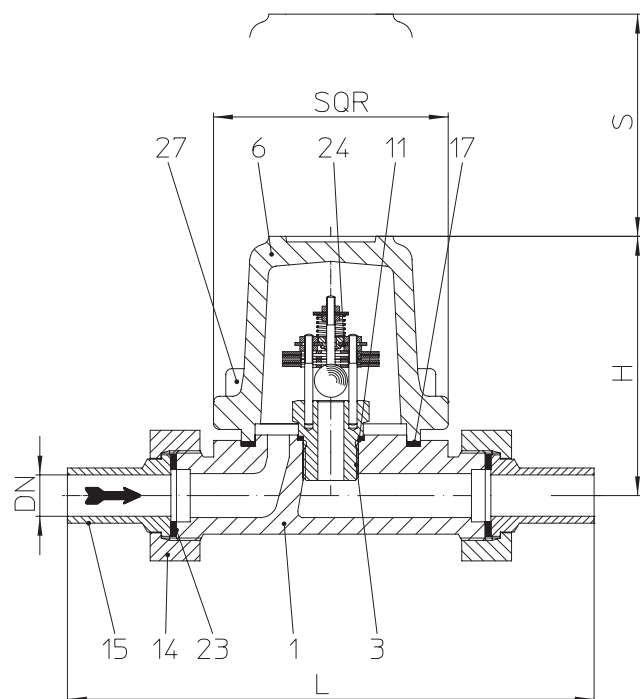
1 mit Schweißverschraubung und Schweißstülle (nur PN16)
